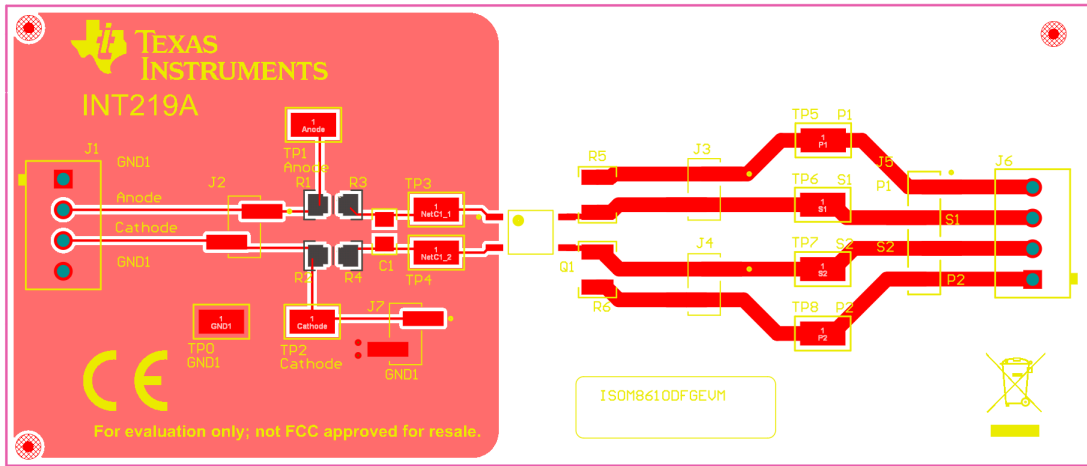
ISOM8610DFGEVM PCB 布局 - 顶层
